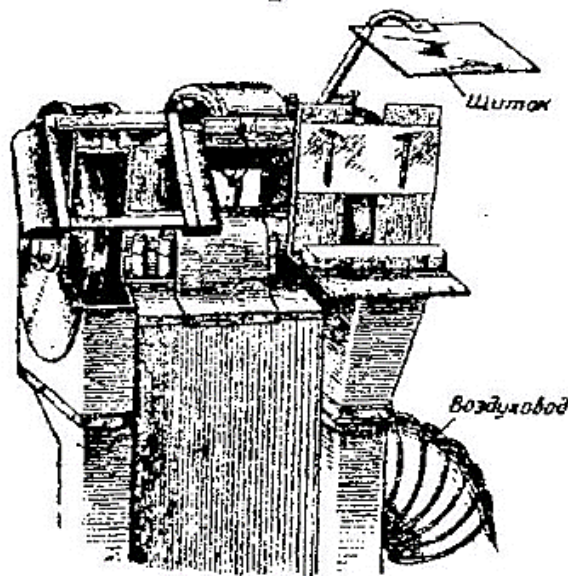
Местная вентиляция для отсоса пыли от наждачной колонки
